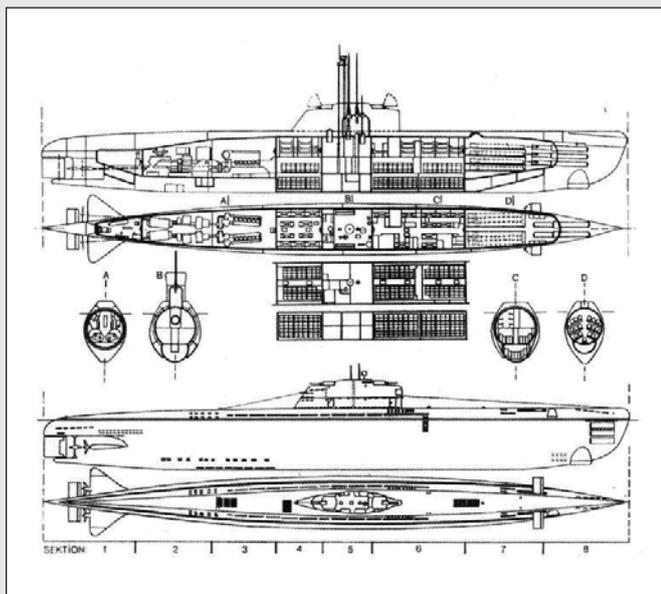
Alzado, planta y disposición interior de los buques Tipo XXI. Son apreciables las secciones del buque, para su construcción modular
